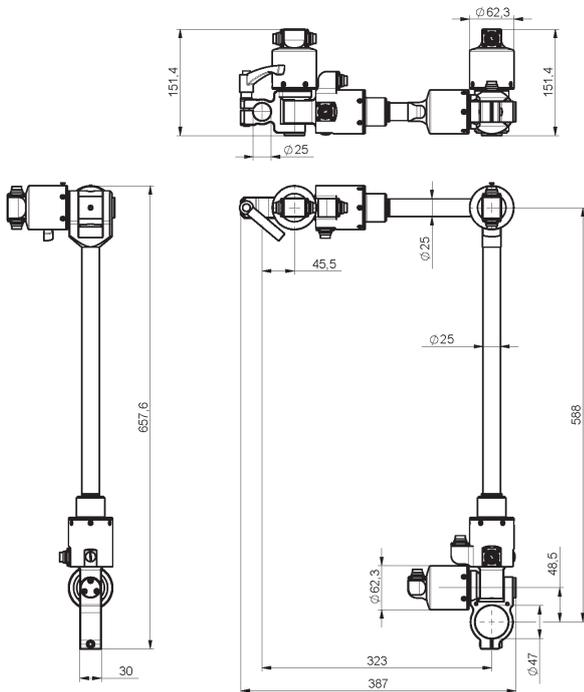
Abmessungen RV-4 Sensor Pkw-Version
